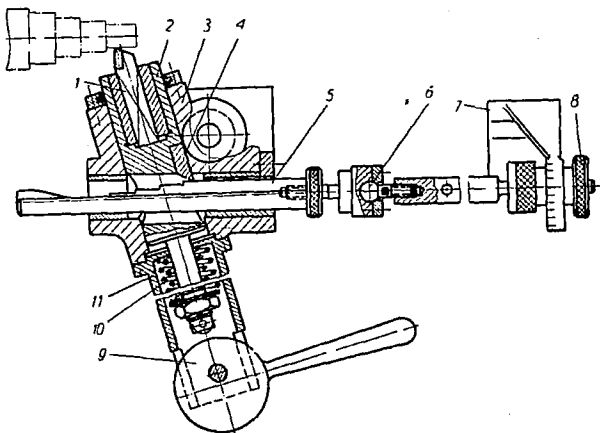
Полуавтоматическое копировальное приспособление для обточки ступенчатых валов.
